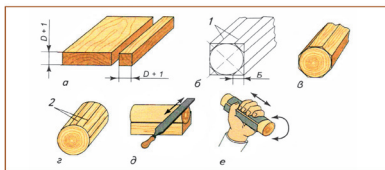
Последовательность изготовления детали цилиндрической формы ручным инструментом:
